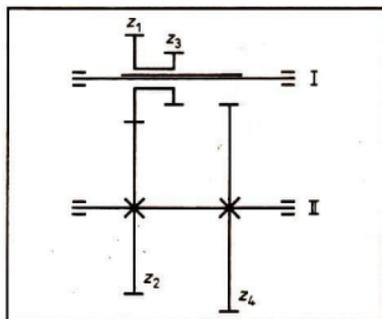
/2 Zahnradgetriebe einer Werkzeugmaschine
